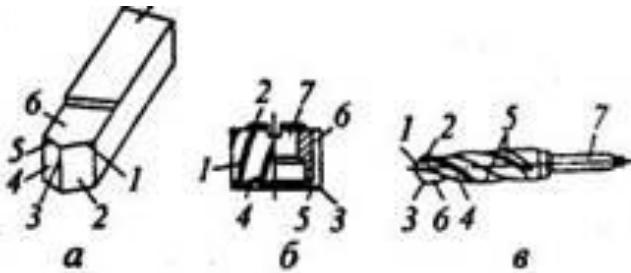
Конструкция и элементы лезвийных режущих инструментов: *a* – токарного резца; *б* – фрезы; *в* – сверла; 1 – главная режущая кромка; 2 – главная задняя поверхность; 3 – вершина лезвия; 4 – вспомогательная задняя поверхность лезвия; 5 – вспомогательная режущая кромка; 6 – передняя поверхность; 7 – крепежная часть инструмента.
